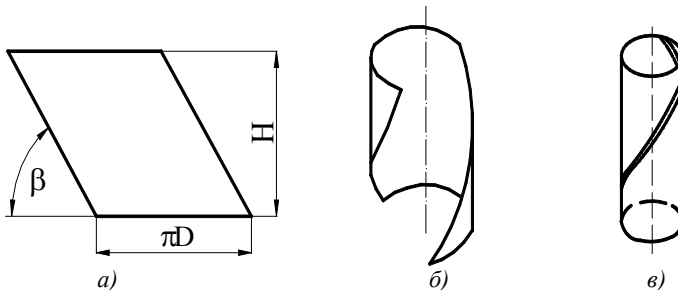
Етапи формування згортної втулки з гвинтовим стиковим швом [8]: а) – заготовка (карточка); б) – часткова згортка втулки; в) – згортна втулка
